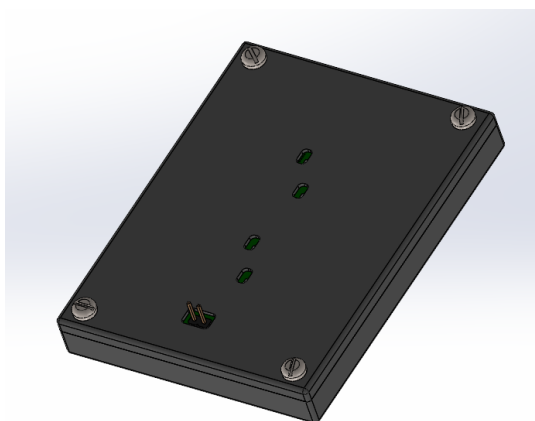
Загальний вигляд корпусу пристрою зверху
